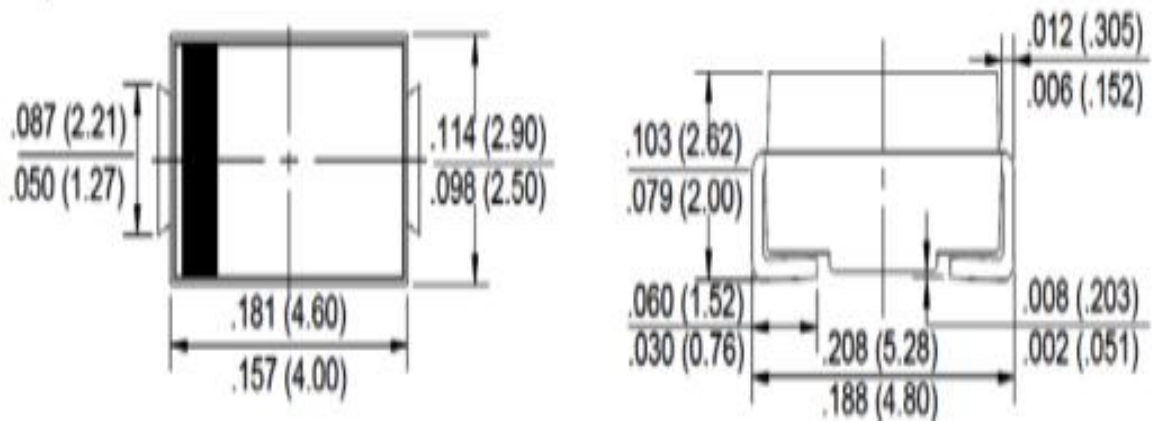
Габаритні розміри діодів з корпусом DO-214
